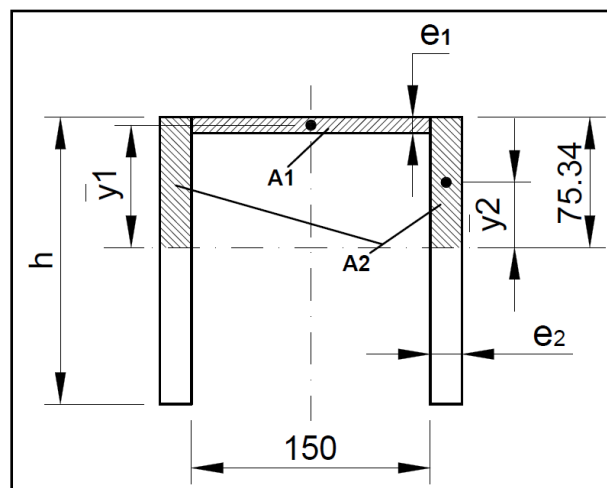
Dimensiones de la sección de la viga horizontal del pórtico – Perfil 1.
